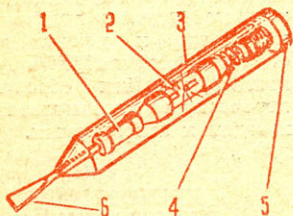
Индикатор напряжения — отвертка: 1 — резистор сопротивлением 2 Мом; 2 — неоновая лампа; 3 — прозрачный корпус; 4 — пружина; 5 — металлический винт; 6 — жало отвертки.
